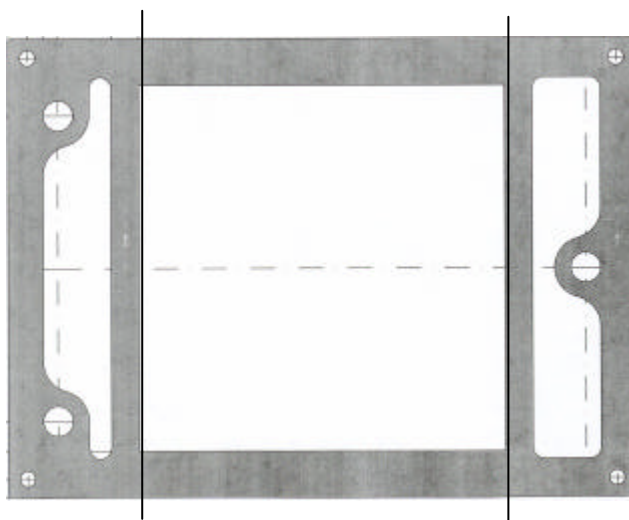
Fügedesign für recheckige Platten im Gegenstromprinzip
